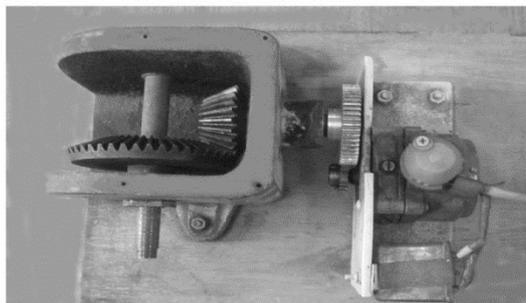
Кинематическая схема привода с коническим зубчатым редуктором:
